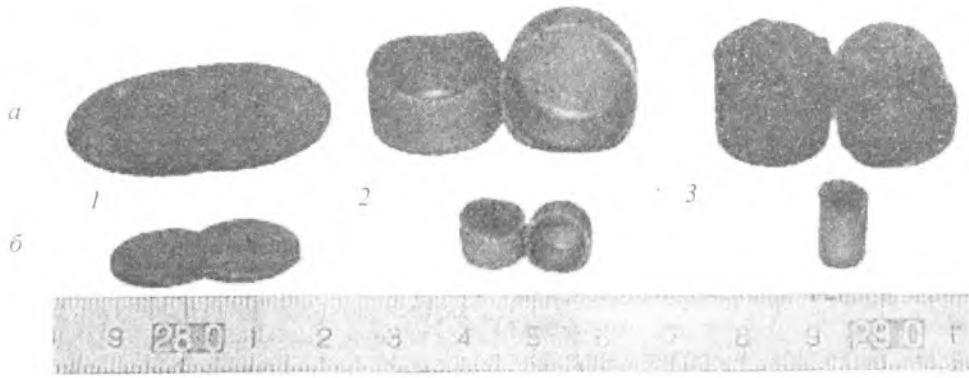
Образцы: 1 – плоская заготовка; 2 – полая заготовка основы после первого перехода вытяжки; 3 – полное композиционное изделие
